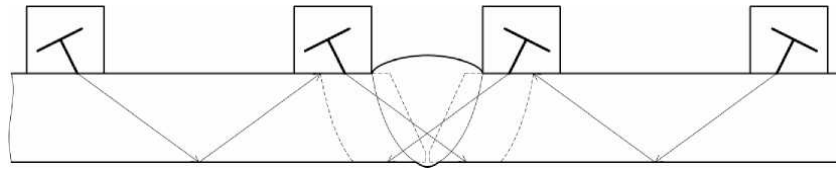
Схема контроля стыковых сварных соединений выполненных односторонней сваркой.
